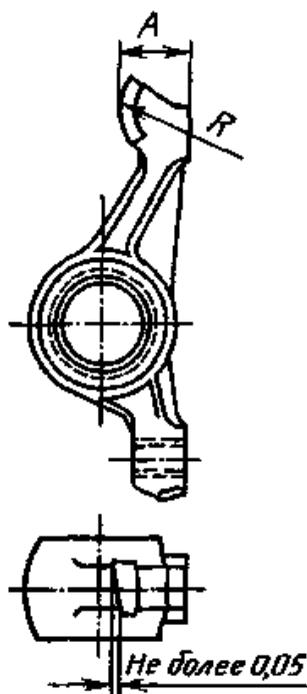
Схема рабочей поверхности бойка коромысла:
